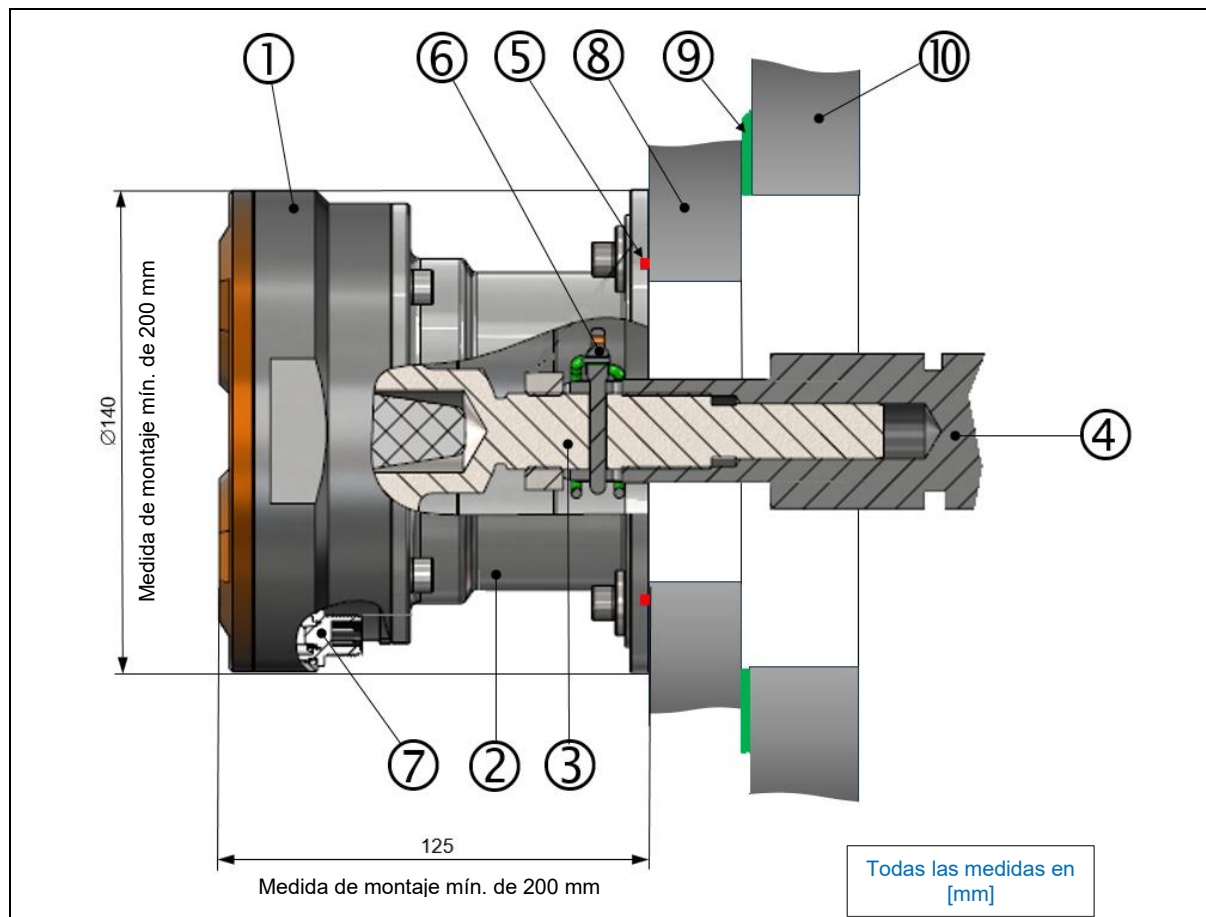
Vista general de los componentes, BEAROMOS® 2020 (versión sin sistema de juntas de cigüeñal)
